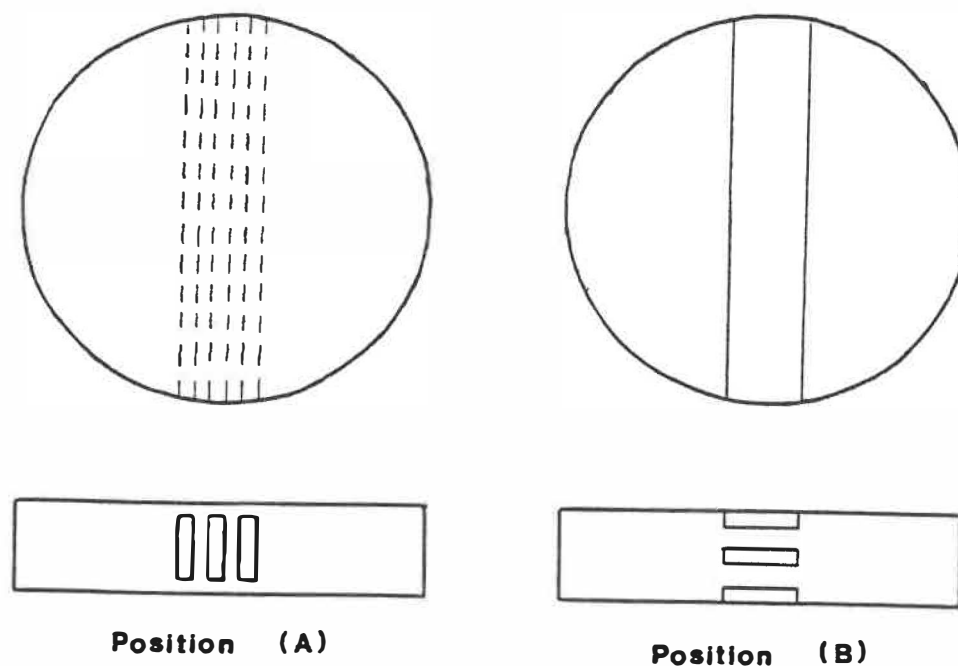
Position des éprouvettes taillées dans la pièce moulée
